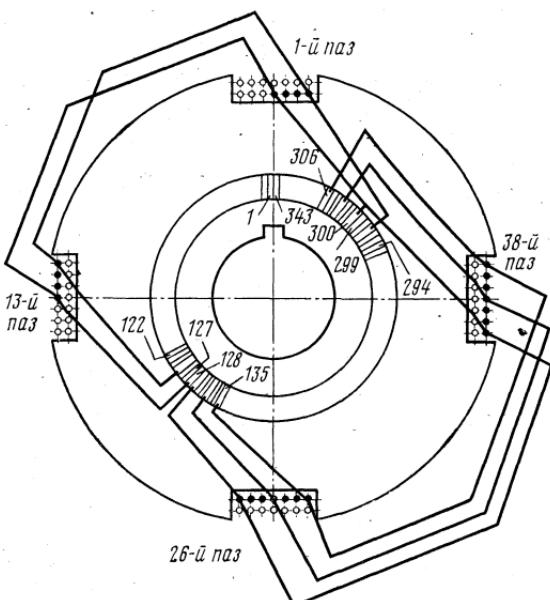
Схема соединения обмотки якоря с коллекторными пластинами электродвигателя НБ-430А
